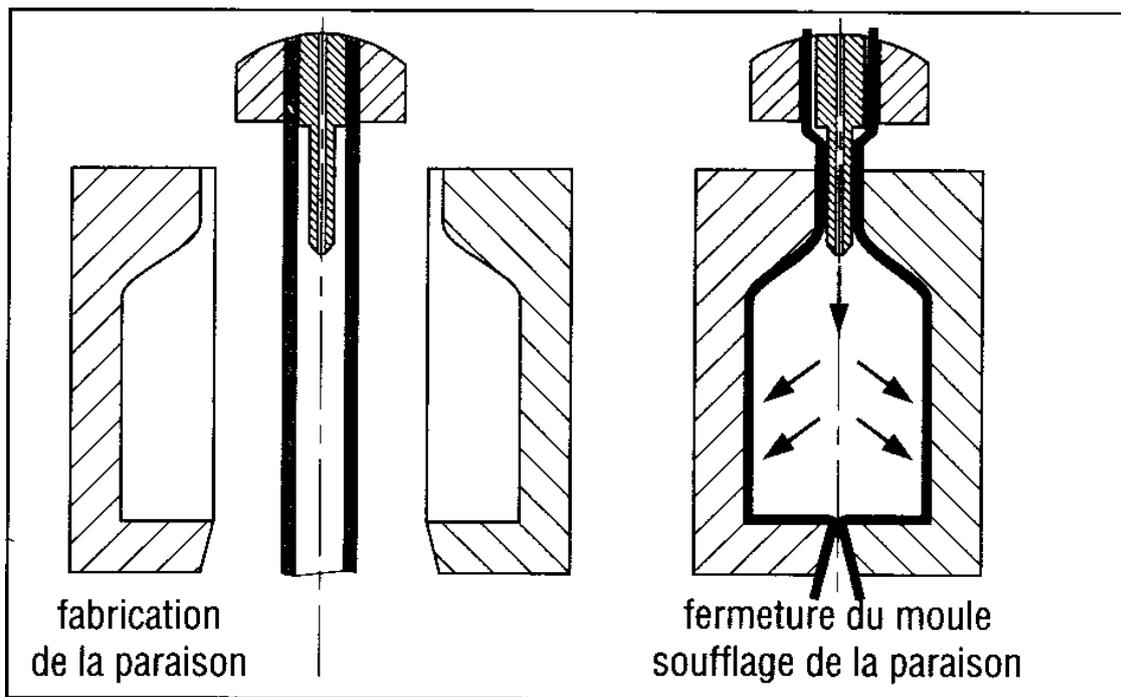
Principe de fabrication d'une bouteille en extrusion-soufflage
